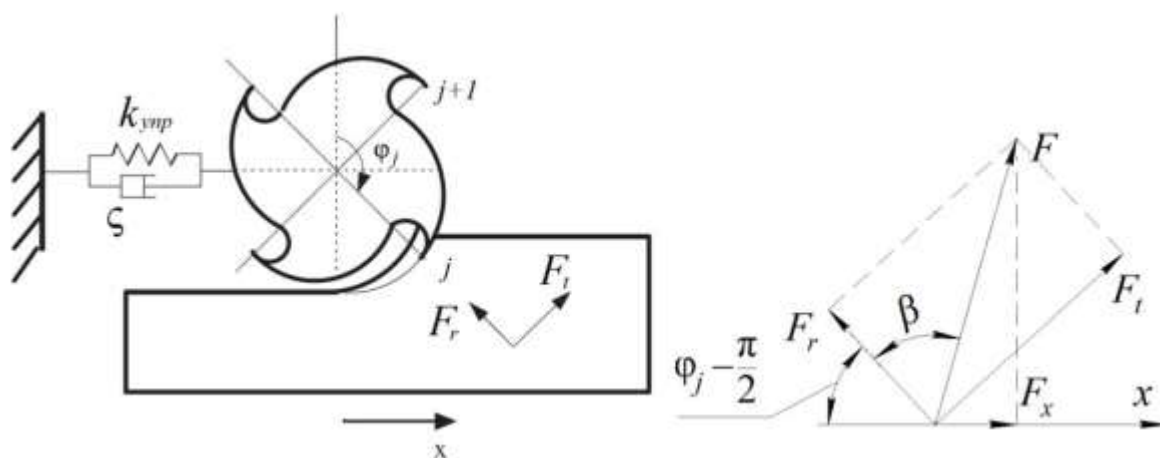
Схема фрезерування з одним ступенем свободи.
